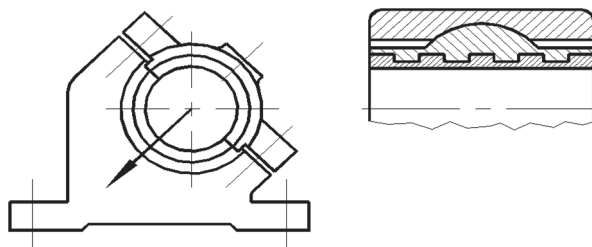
Разъемный самоустанавливающийся подшипник
